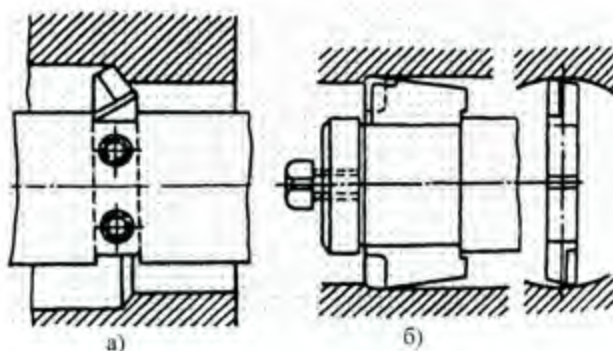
Схема закріплення різця (а) і розточувальної пластини (б) у борштанзі
